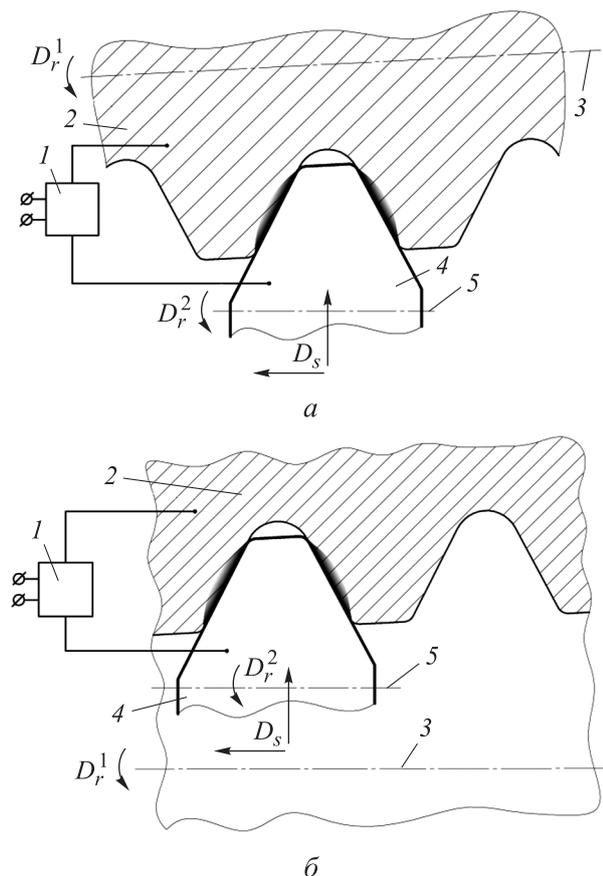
Схемы финишной ЭМО конической замковой резьбы ниппеля (а) и муфты (б) переводника:
